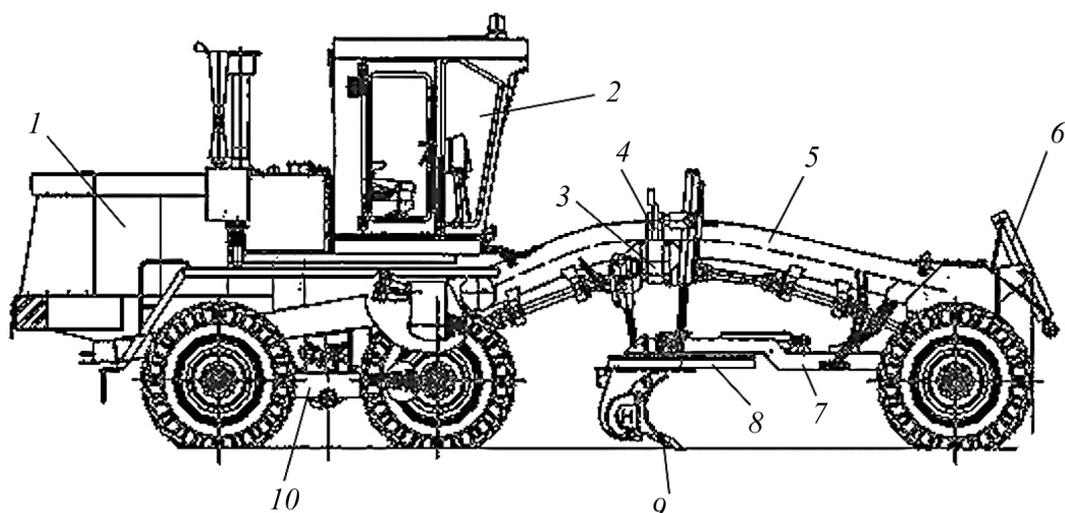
Автогрейдер ДЗ-122Б: 1 – двигатель; 2 – кабина; 3 – редуктор подъема; 4 – механизм поворота; 5 – основная рама; 6 – гидроцилиндр передней навески; 7 – тяговая рама; 8 – поворотный круг; 9 – отвал; 10 – балансир
